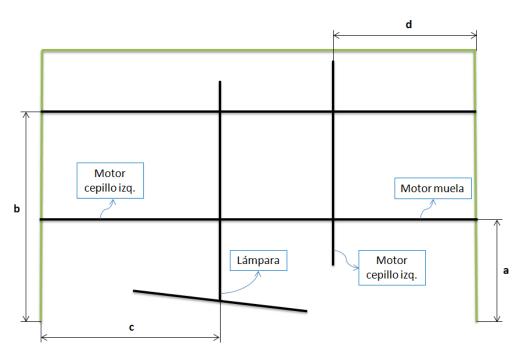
Vista en planta del puesto y la ubicación de las barras
